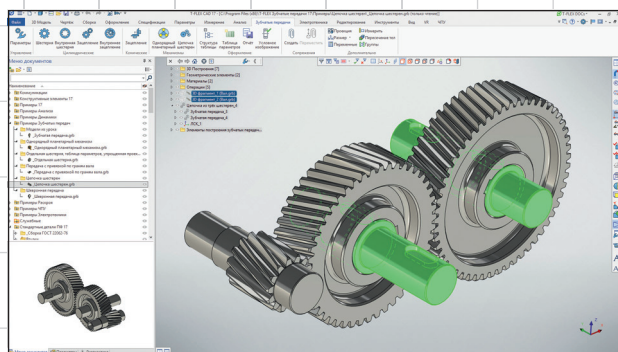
Цепочка шестерен, построенная инструментами T-FLEX Зубчатые передачи
